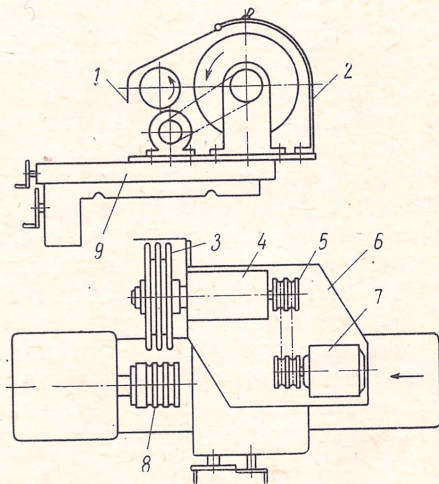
Приспособление к токарному станку для полирования цилиндрических поверхностей
